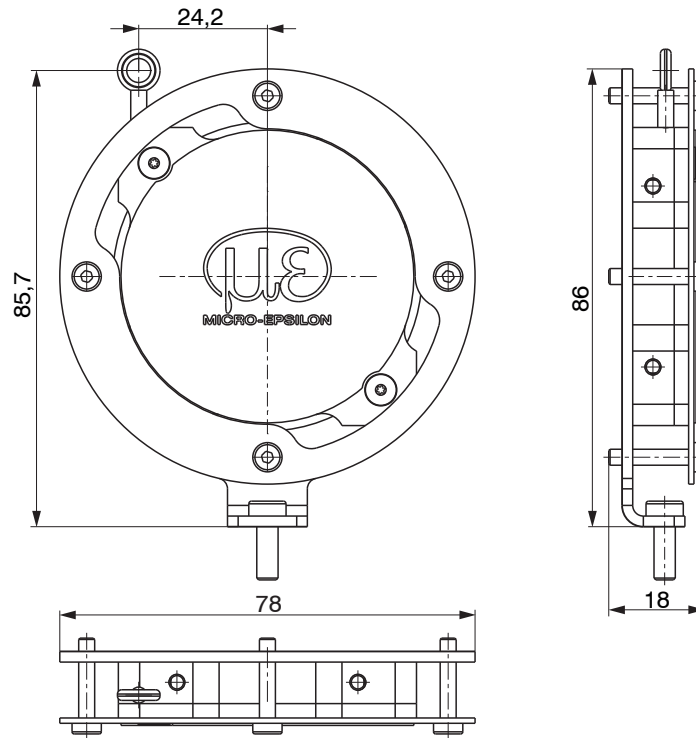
Maßzeichnung WDS-MB56 Montagewinkelset - Seitenansicht, Abmessungen in mm
